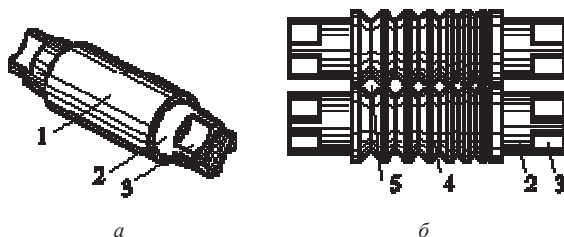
Валки прокатных станов: *а* – гладкий валок, *б* – калиброванные валки с ромбическими калибрами; 1 – бочка (боковая поверхность гладкого валка); 2 – шейка (предназначена для закрепления валка); 3 – трефа (предназначена для передачи вращательного движения от привода к валку); 4 – ручей (вырез на поверхности валка); 5 – калибр (зазор заданной формы между валками)
